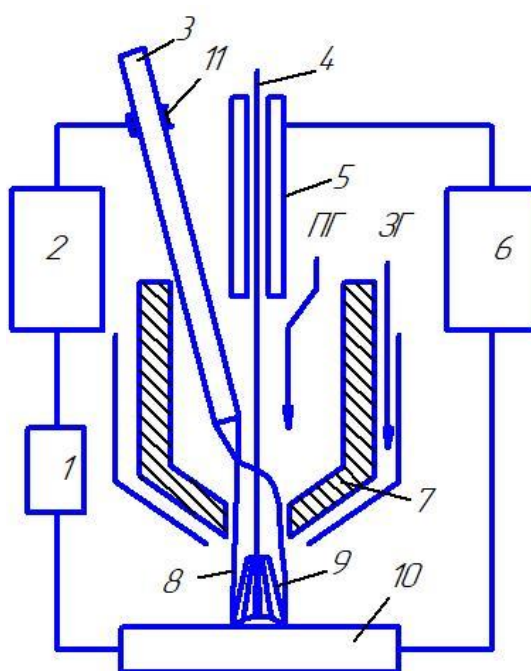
Схема плазменной сварки-наплавки плавящимся электродом
